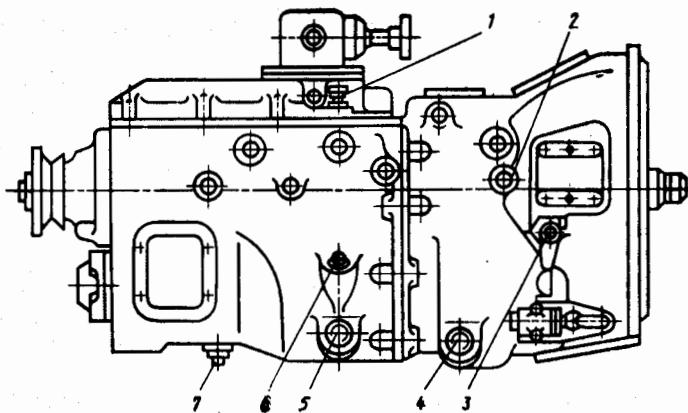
Точки смазывания сцепления и коробки передач с делителем автомобилей КамАЗ:
